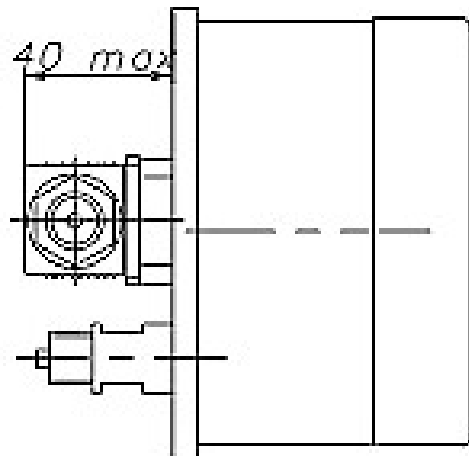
(лист 1 из 2) – Присоединительные и габаритные размеры манометра
